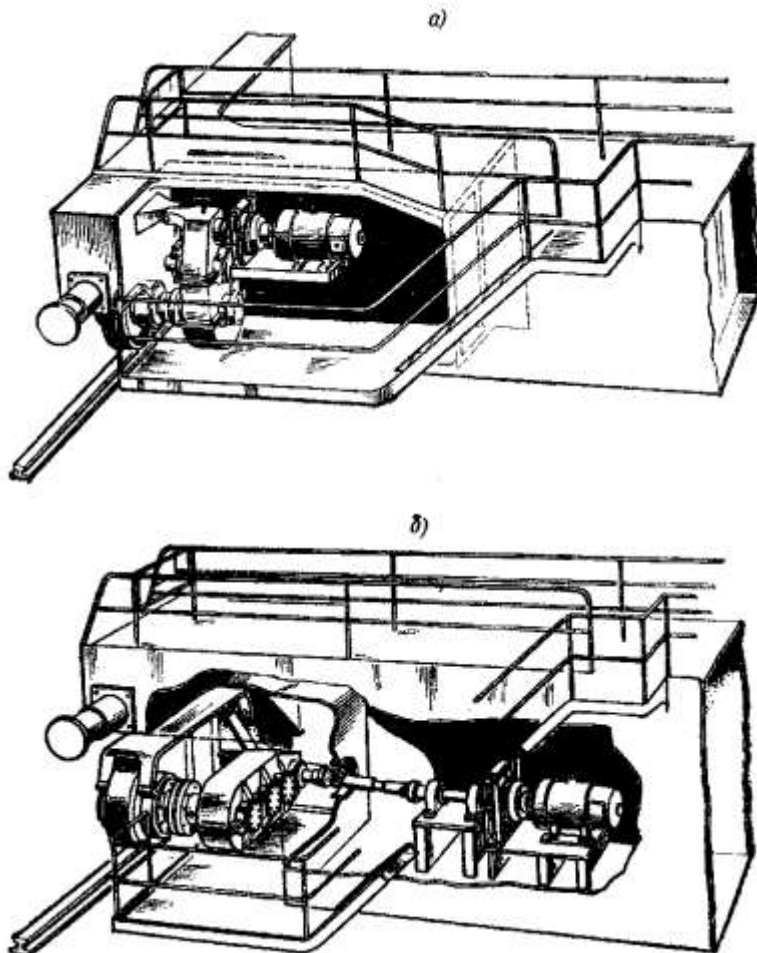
Установка раздельного привода механизма передвижения мостового крана: а – с вертикальным редуктором; б – с горизонтальным редуктором
